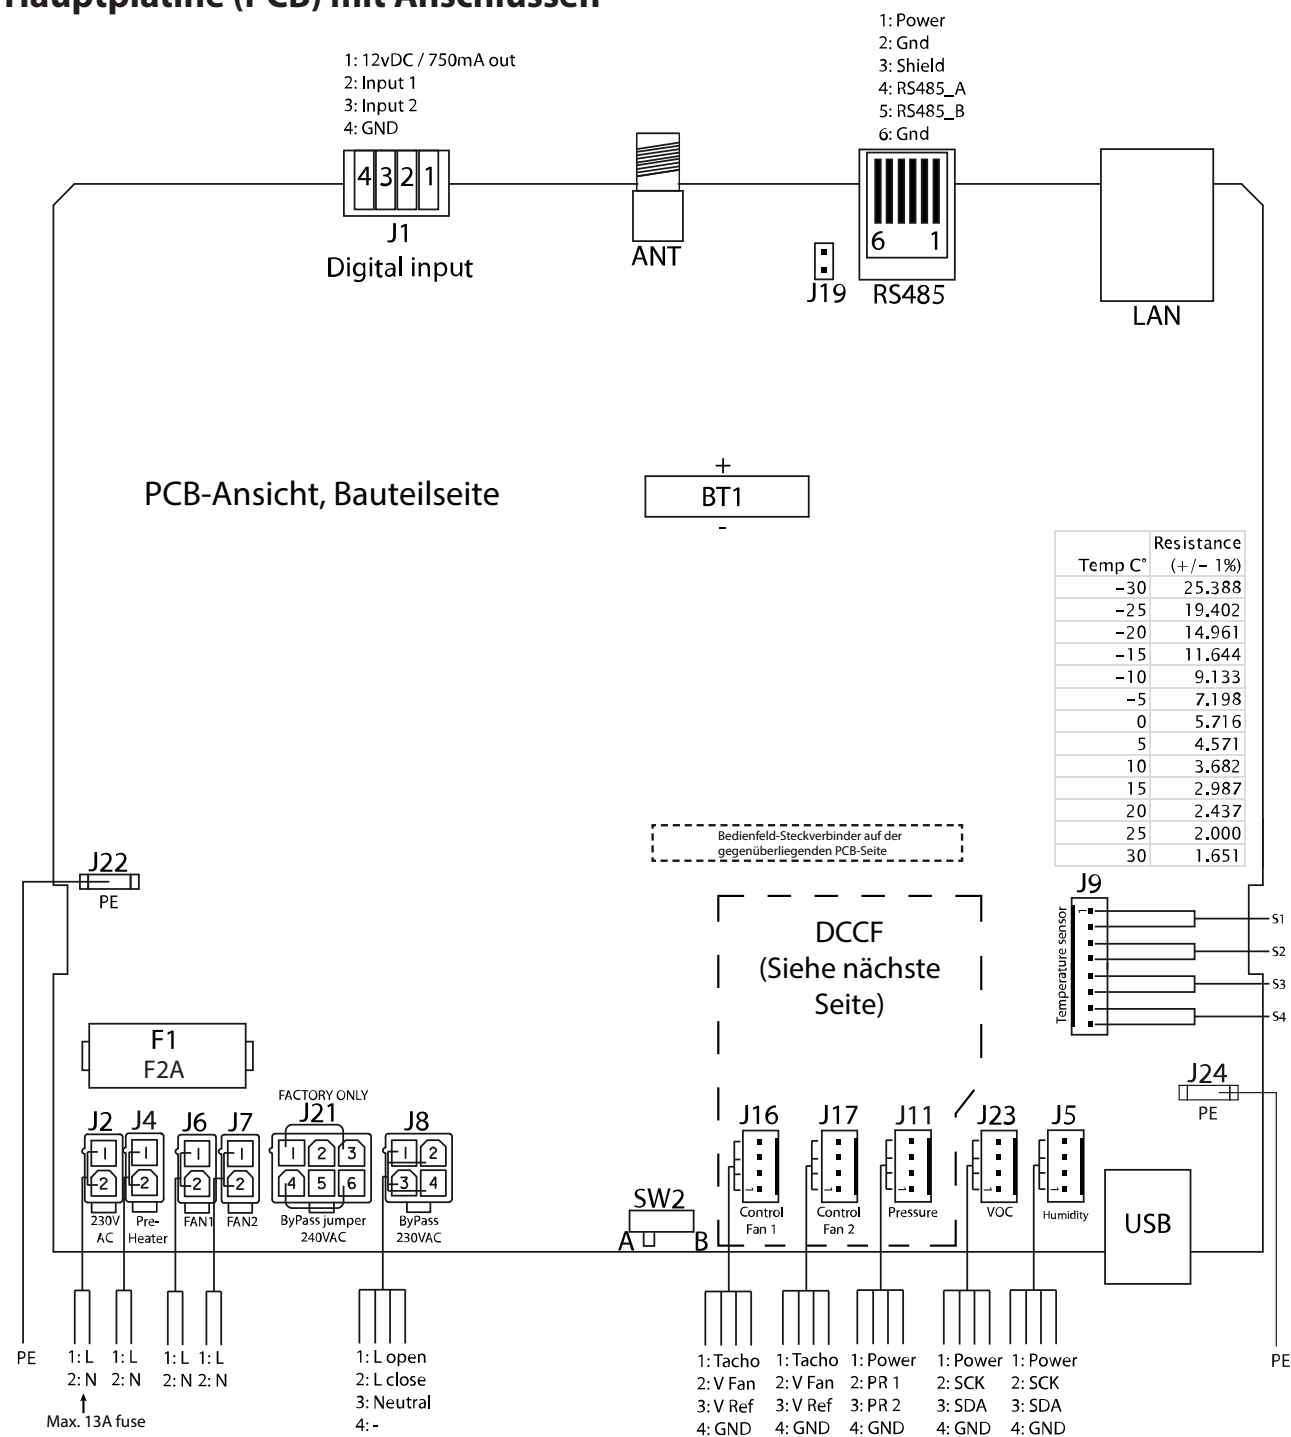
Hauptplatine (PCB) mit Anschlüssen
